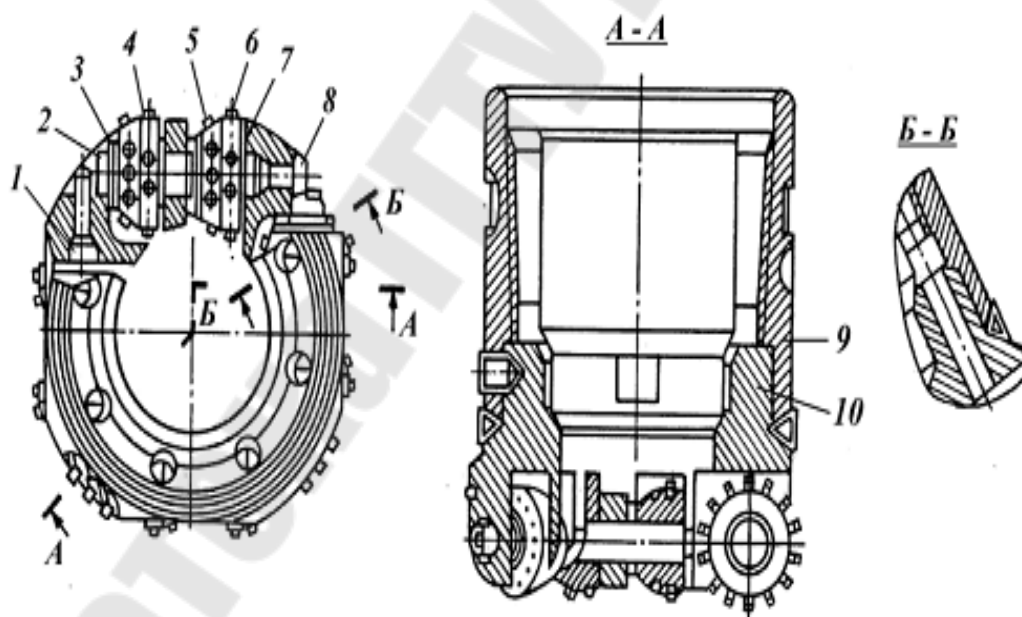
Восьмишарошечная бурильная головка режущего действия, с шарошками, оснащенными твердосплавным, карбидвольфрамовым вооружением (зубками): 1 – запорный хвостовик; корпус; 2 – опорная ось; 3 – шайба; 4 – скважинообразующая шарошка; 5 – калибрующие твердосплавные подрезные зубки с плоской рабочей частью; 6 – основные режущие твердосплавные клиновидные зубки, формирующие керн (шарошкой 7) и скважину (шарошкой 4); 7 – кернообразующая шарошка; 8 – запорный винт; 9 – присоединительная головка с конической замковой резьбой; 10 – корпус
